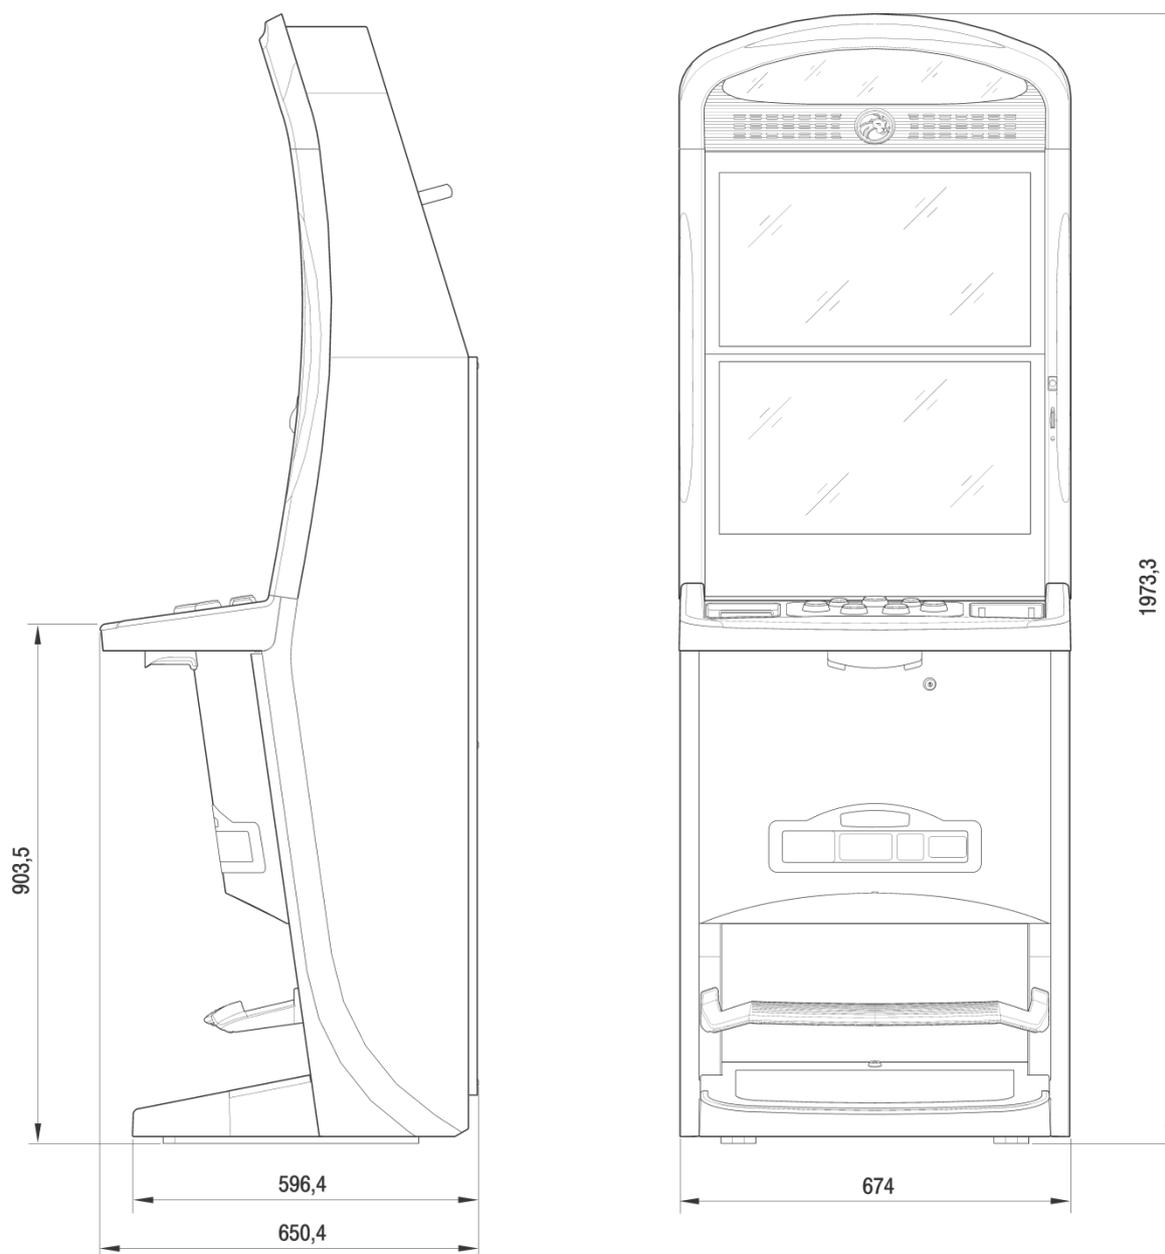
Dimensiones de la máquina NOVO GIGA STAR HD Premium (FV550 F2)
